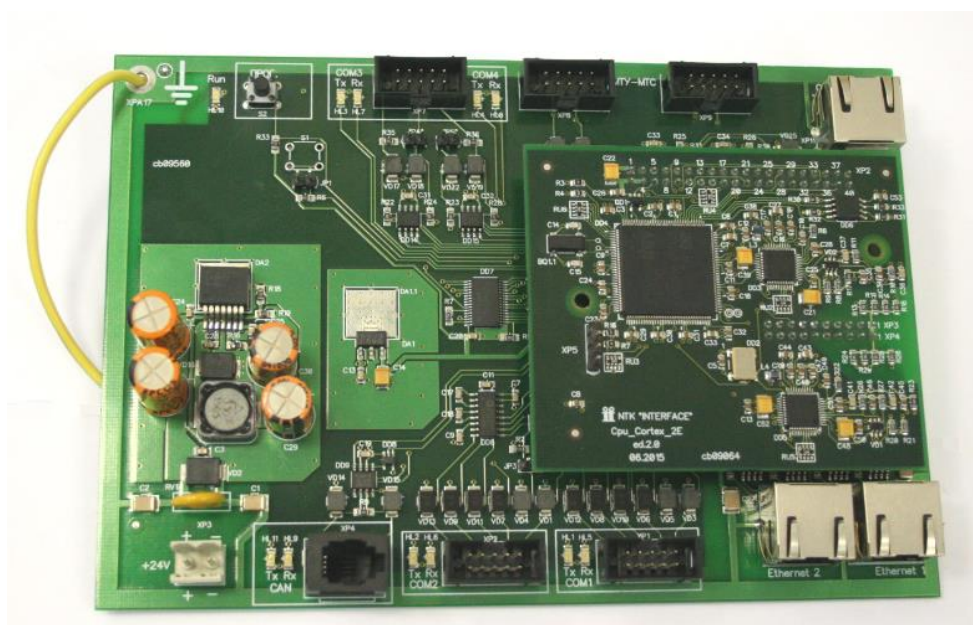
Внешний вид «Синком-ДК» (версия 2, без корпуса, с процессорным модулем)
